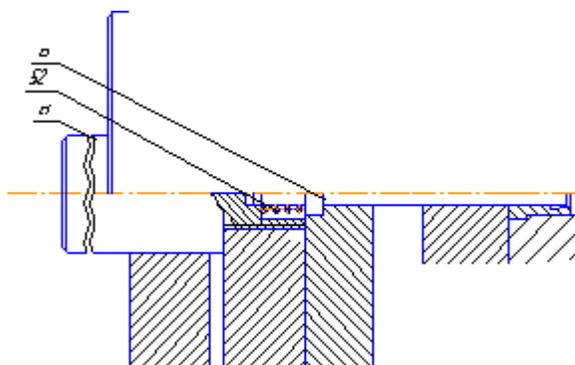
Конструкция толкателя литниковой системы — “стреляющего”
